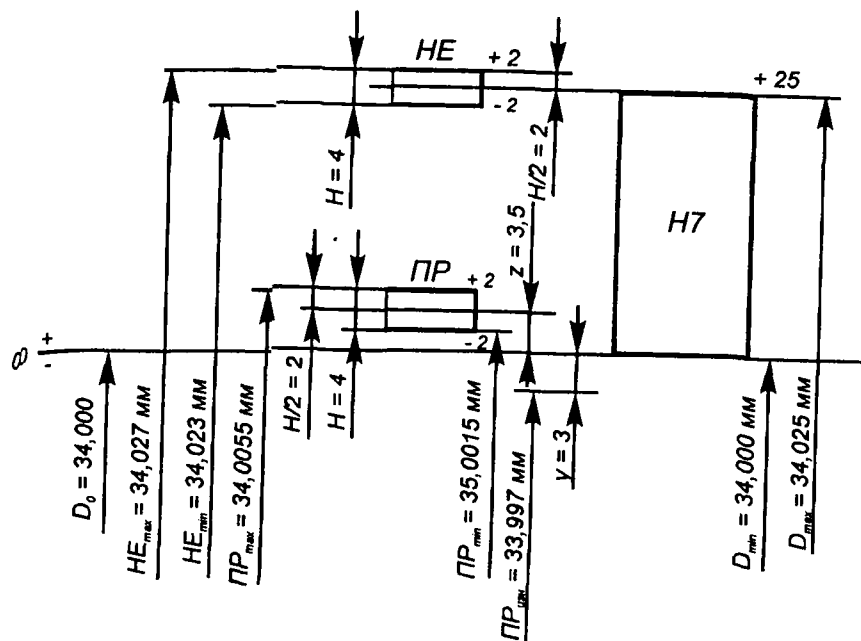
Схема расположения полей допусков калибров для контроля отверстия  $\varnothing 34H7$
